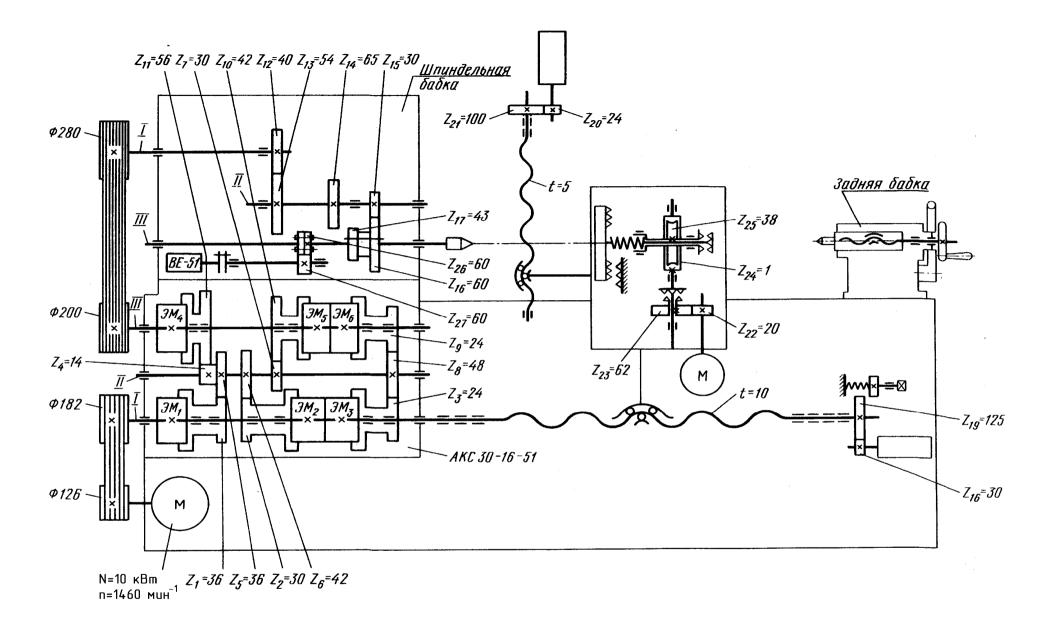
Кинематическая схема станка с ЧПУ 16К20Ф3
